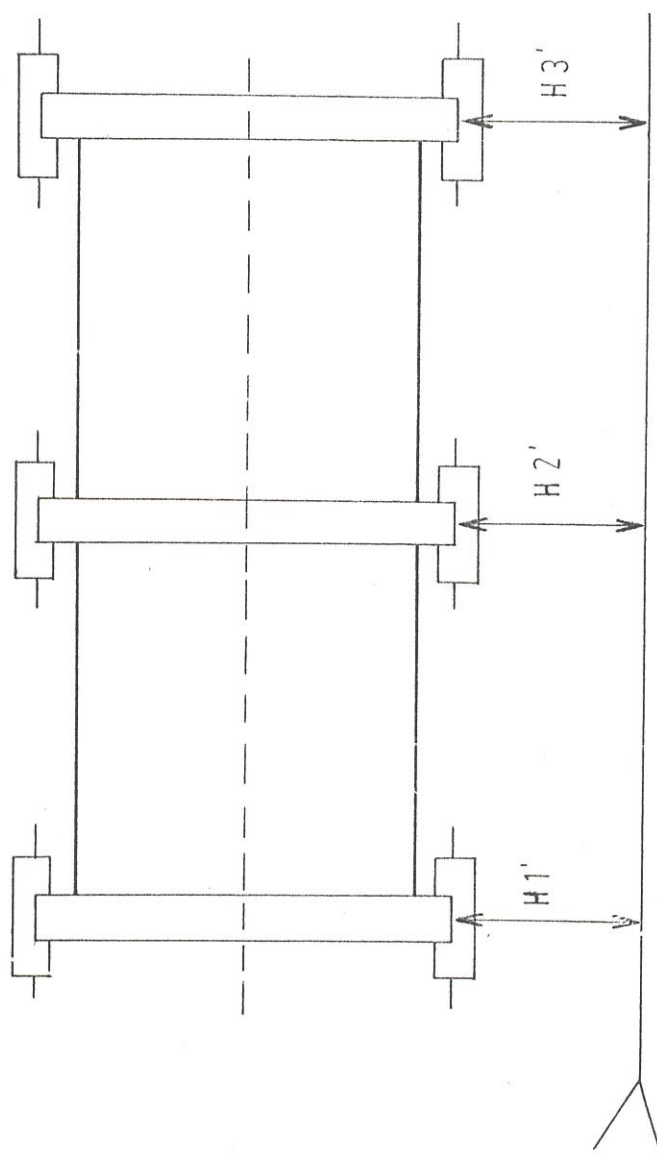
MEDICION DEL PLANO HORIZONTAL CON TEODOLITO JUNTO
